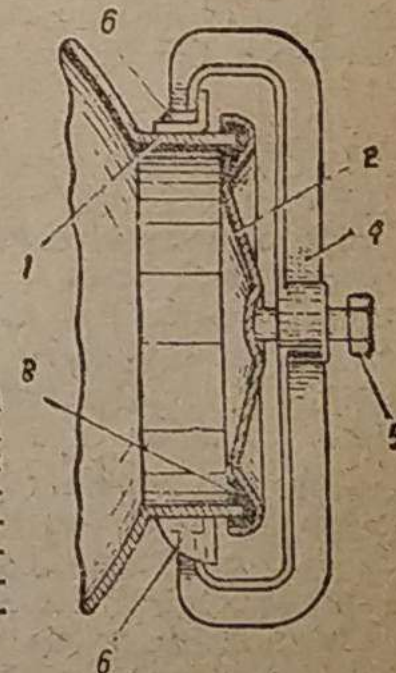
Боковой люк газогенератора ГАЗ-42: 1 — кромки люка, 2 — крышка люка, 3 — уплотнительный шнур, 4 — накидная скоба, 5 — нажимной болт, 6 — опорные лапки скобы.
